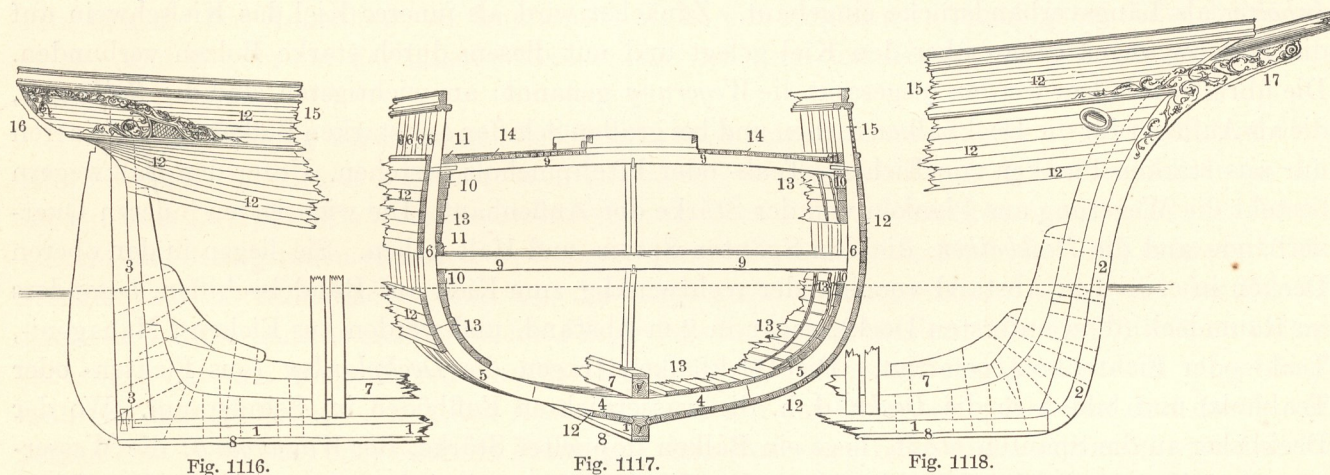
1118. Hölzernes Schiff (1 Kiel, 2 Vorsteven, 3 Achtersteven, 4 Bodenwrangen, 5 Kimmstücke, 6 Auflanger, 7 Kielschwein, 8 Loskiel, 9 Deckbalken, 10 Balkweger, 11 Wassergänge, 12 äußere Beplankung, 13 innere Beplankung, 14 Oberdeckbeplankung, 15 Reling, 16 Heck, 17 Galion).
